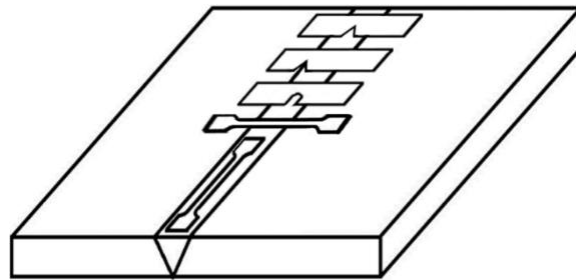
Схема выреза образцов из СС для испытаний на растяжение и ударный изгиб.
